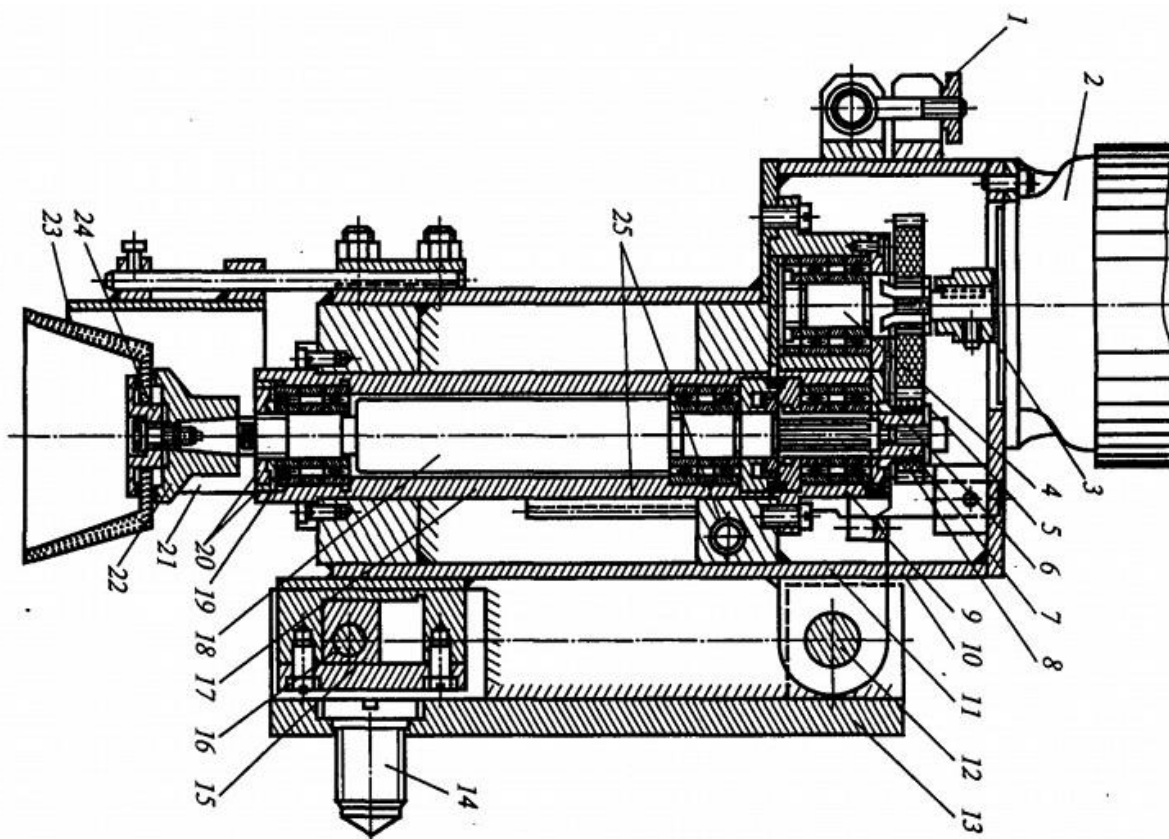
Стационарное приспособление для восстановления направляющих шлифованием или фрезерованием:
